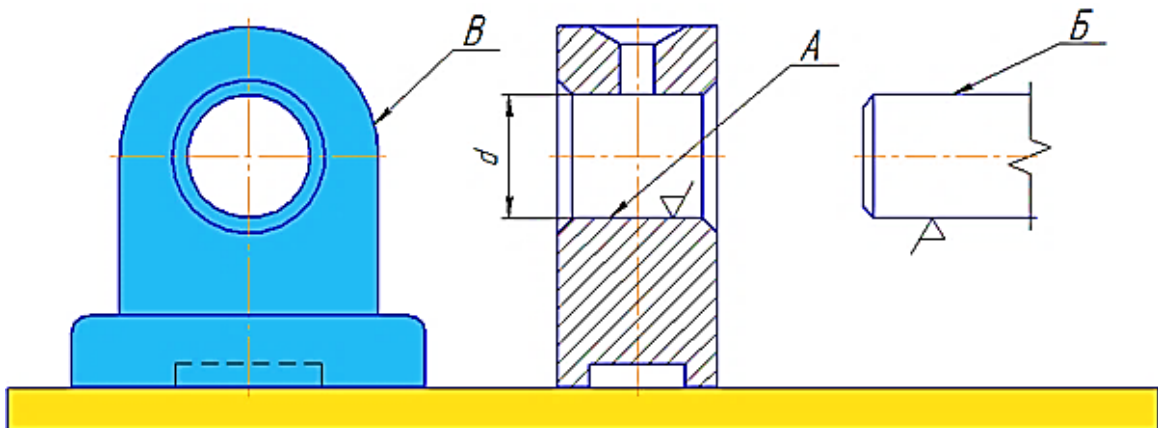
Образец простановки размеров элементов сопряжённых деталей *A* – охватываемая поверхность; *B* – охватывающая поверхность; *B* — свободная поверхность; *d* – номинальный размер.
